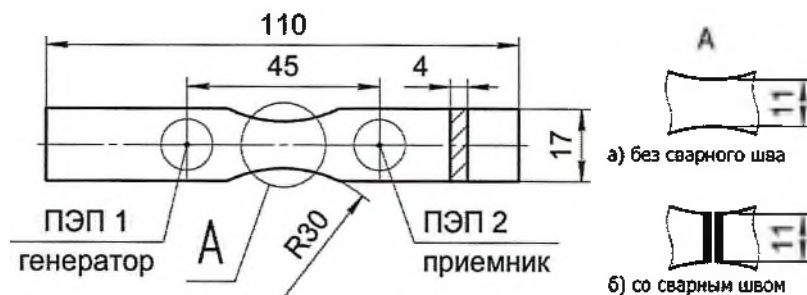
Образец высокопрочного алюминиевого сплава В96 в виде лопаток двух типов: (а) без сварного соединения и (б) со сварным швом.
